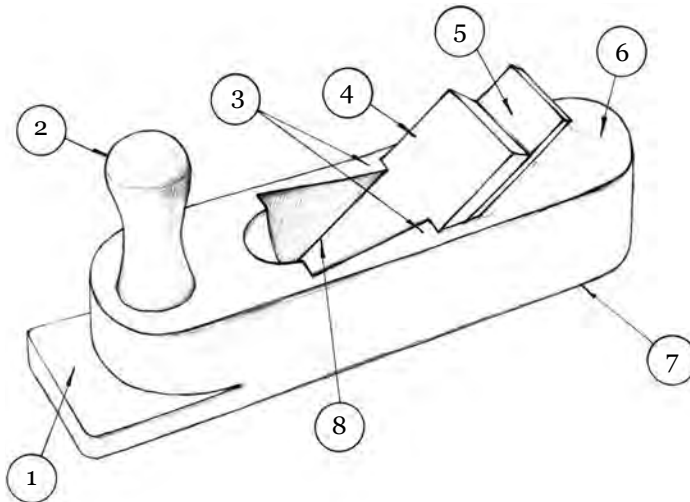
Названия элементов рубанка: 1 — нос; 2 — рукоятка; 3 — заплечики; 4 — клин; 5 — нож; 6 — задняя «бабка»; 7 — колодка; 8 — зев
